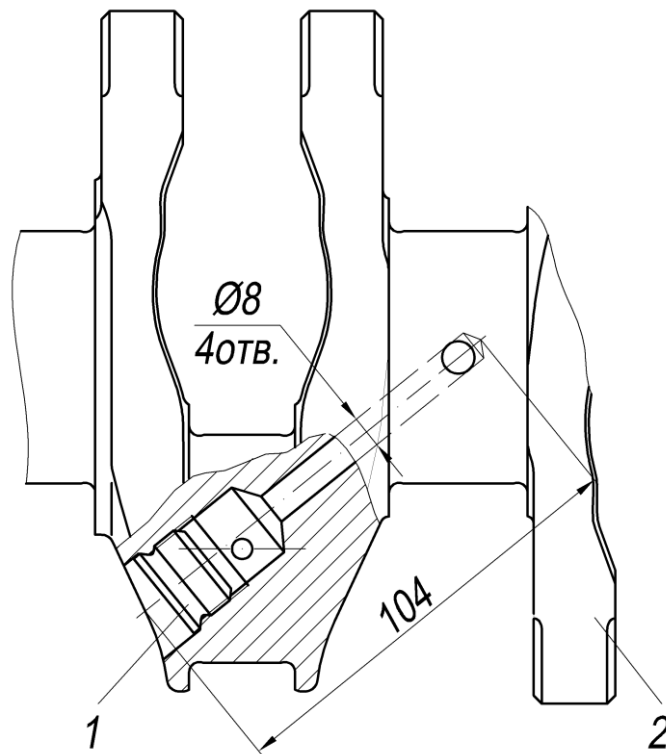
Шатунная и коренные шейки коленчатого вала с каналом для смазки шеек вала
